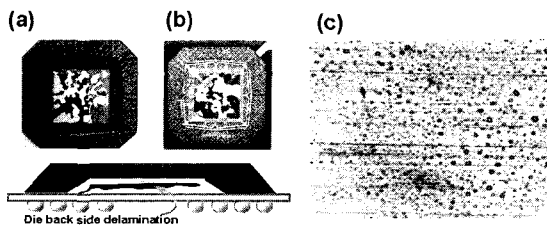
Chip backside delaminated sample when using PCB type B for PBGA (a) backside of the Chip with adhesive residue (b) PCB side (c) Optically magnified photo of Si chip back side (100x).
